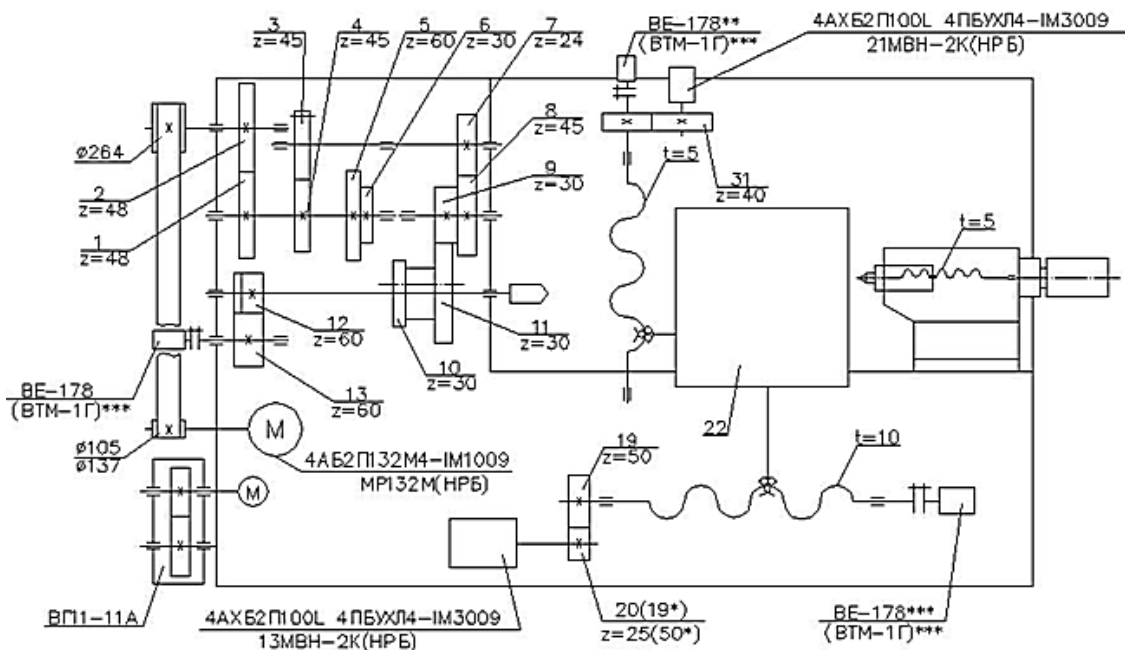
Кинематическая схема станка 16K20Ф3
